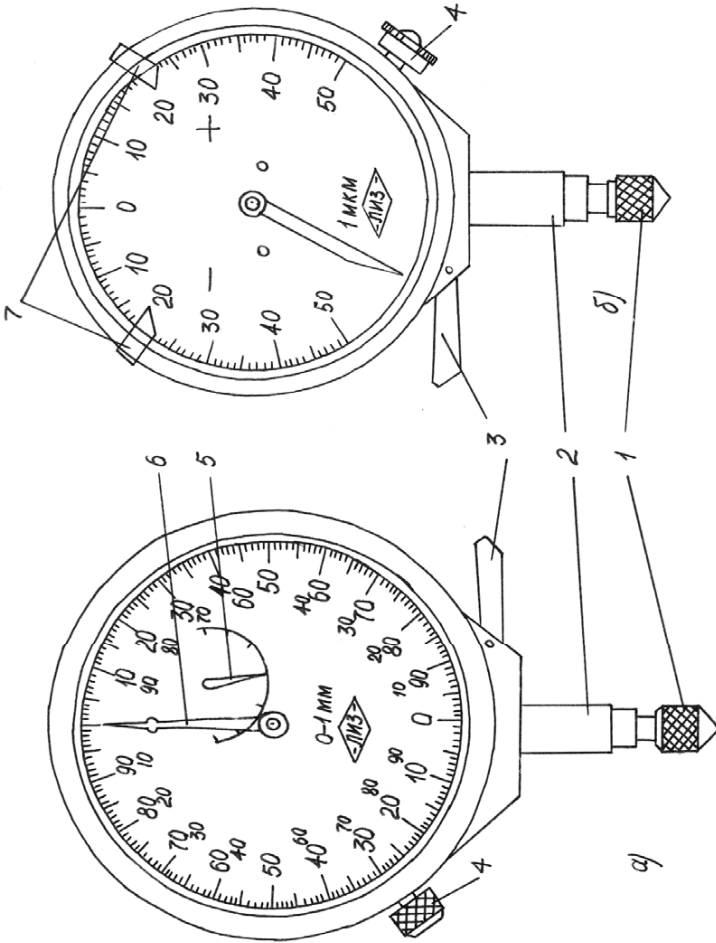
Вазгільно-зубчасті головки ІГ; а – базгільно-зубчасті головки ІГ; б – одгильно-зубчасті головки ІГ; 1 – кінцевик; 2 – гільза; 3 – відводка; 4 – гвинт; 5 – показчик кількості обертів; 6 – стрілка основна; 7 – показчик межі допуску
